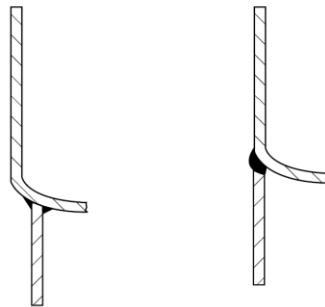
Tipos de soldadura en el soporte de falda [1]
